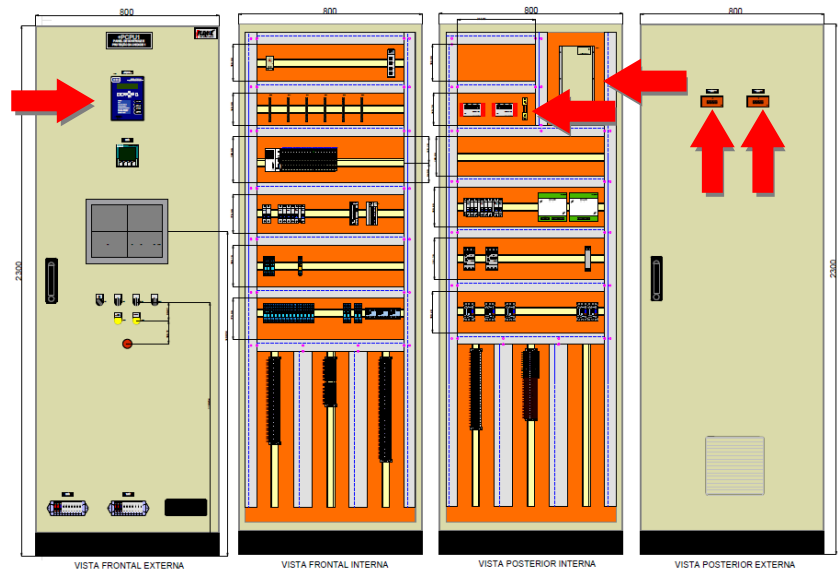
Layout De Fabricação Dos Painéis Do Projeto C.
